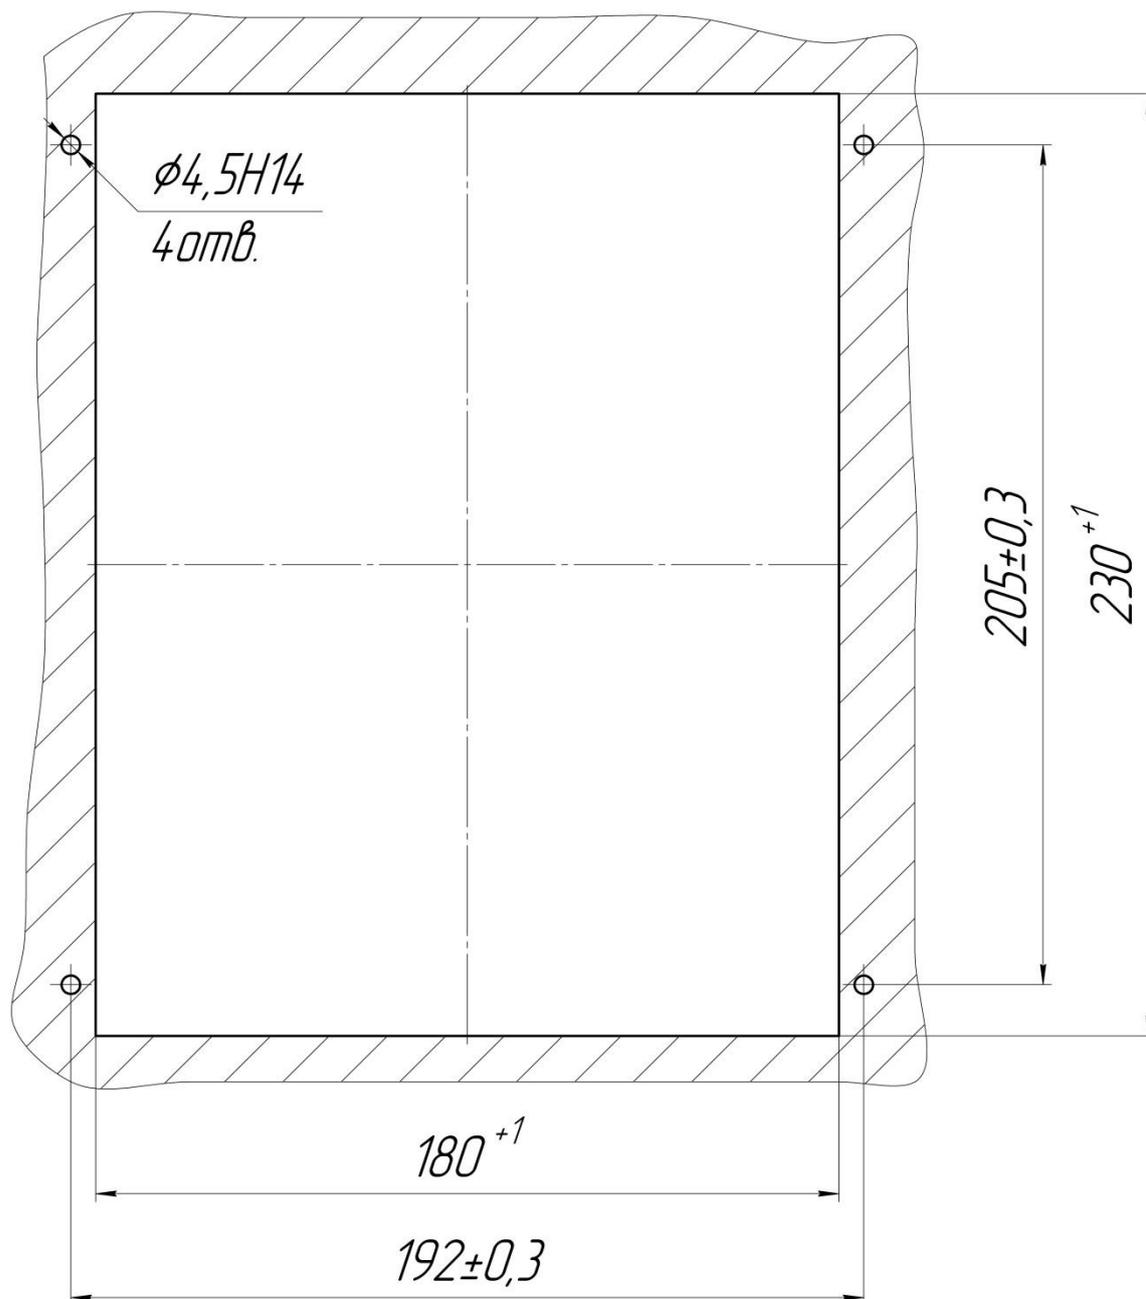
Габаритные размеры окна и крепежных отверстий для установки РЗЛ-05.РПН, РЗЛ-05.РПН01
